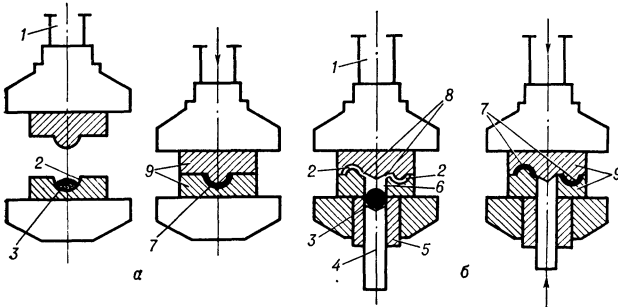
Схема процессов формирования изделий из реактопластов (а — компрессионное прессование; б — литьевое прессование): 1 — верхний плунжер; 2 — оформляющие гнезда прессформы; 3 — перерабатываемый материал; 4 — поршень; 5 — трансферный цилиндр; 6 — загрузочное отверстие; 7 — изделие; 8 — литниковые каналы; 9 — прессформа.
